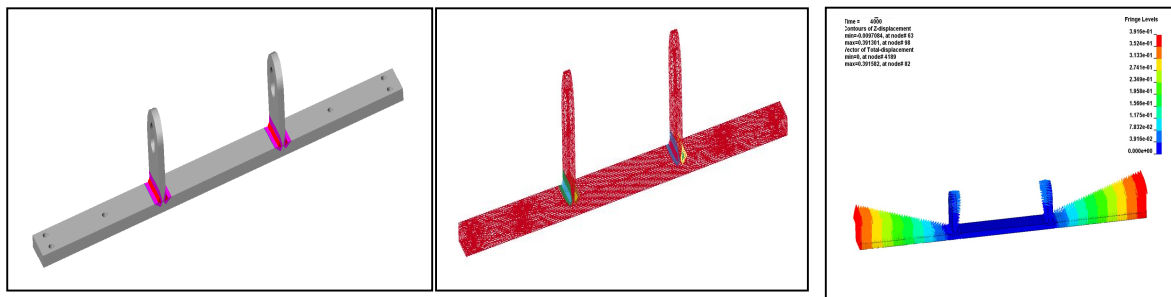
Трёхмерные твердотельные и конечно-элементные модели сварной конструкции
